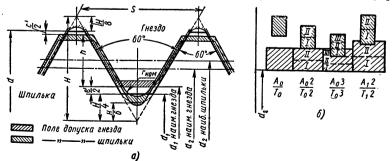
Допуски метрической резьбы с натягами: a — общая схема; δ — схема расположения полей допусков среднего пламетра
